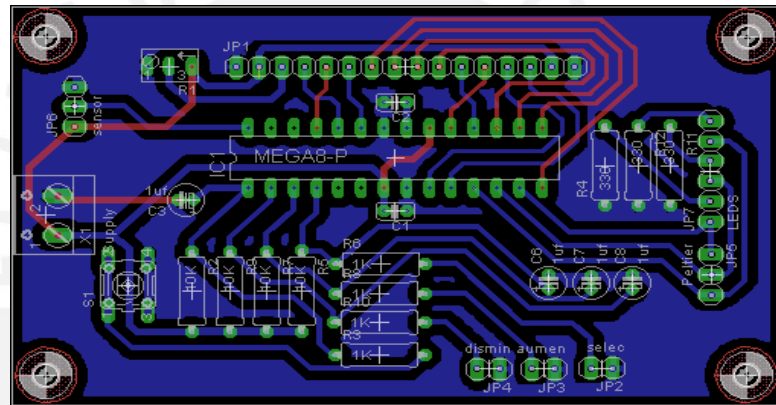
BOARD de la tarjeta principal [elaboración propia].
